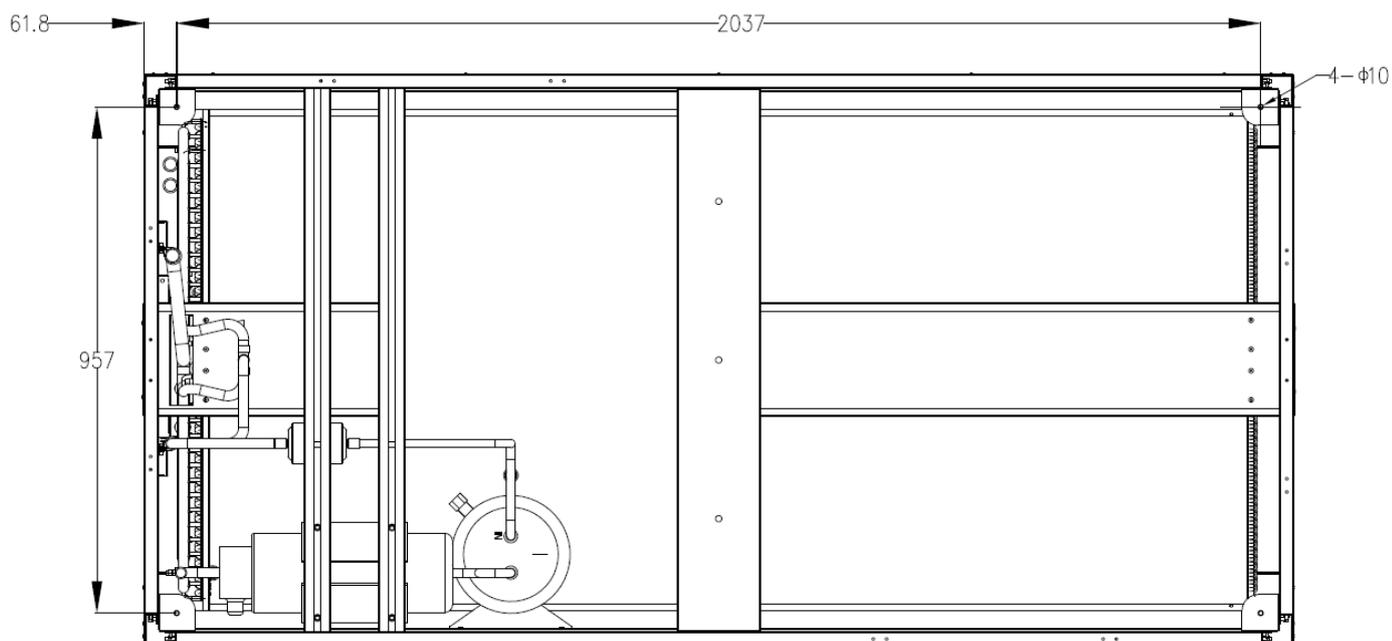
Монтажные размеры нижней части блока с двумя вентиляторами
